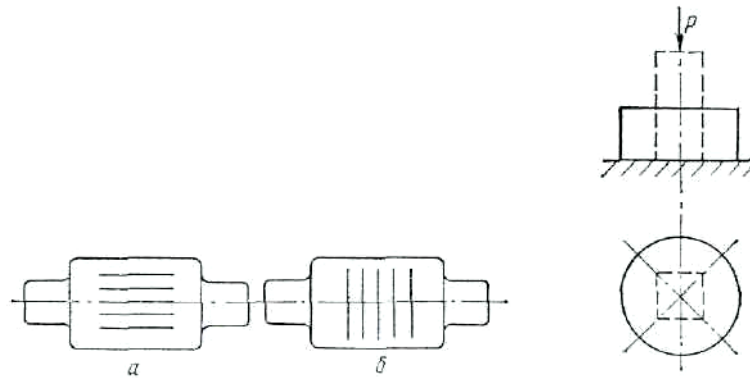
Валок з поперечними (а) і круговими (б) насічками і схема осадки прямокутного зразка
